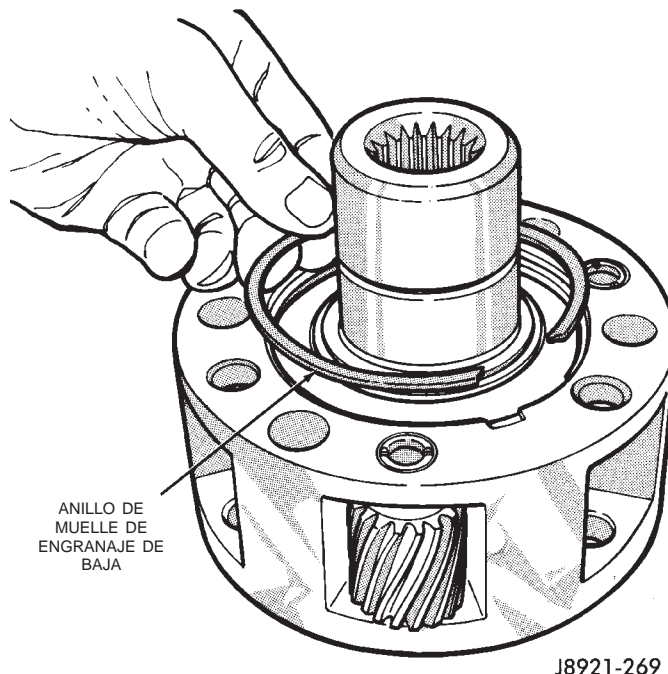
Desmontaje e instalación de anillo de muelle de engranaje de baja
